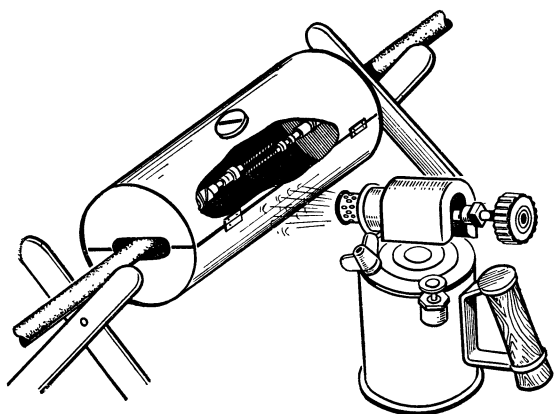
Кожух металлический для обогрева клеевых швов
